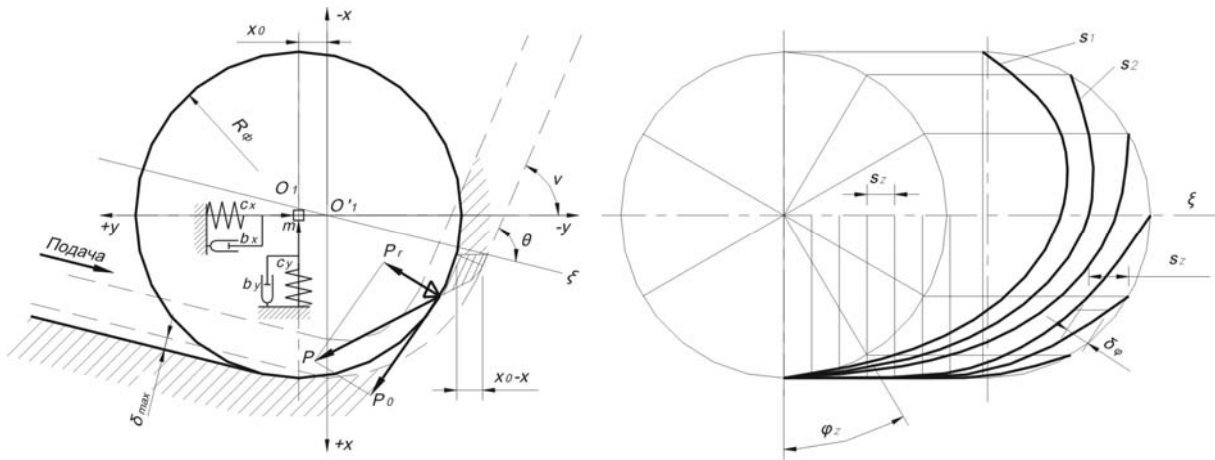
Силовая схема фрезерования и траектория зубьев фрезы
